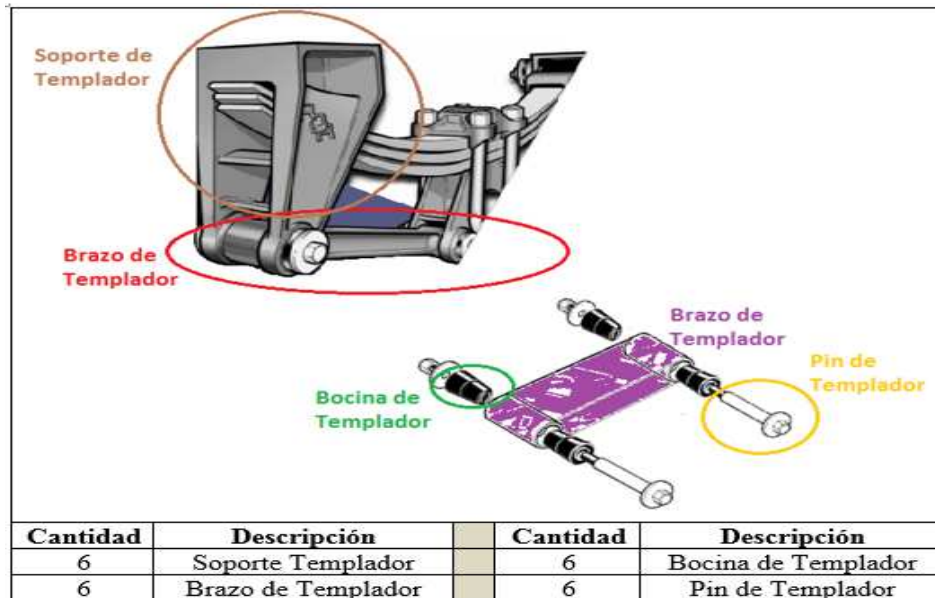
Partes del templador del sistema de suspensión mecánica del remolque
